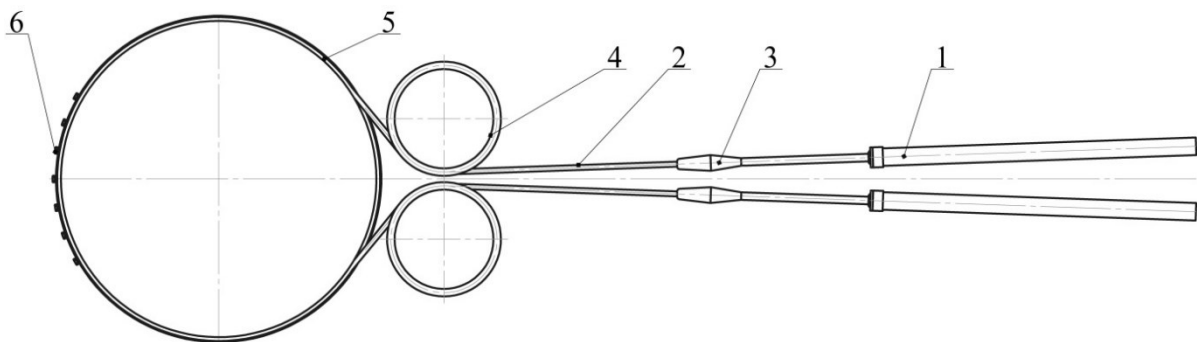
Опорно-поворотное устройство машины СЗП-600:
